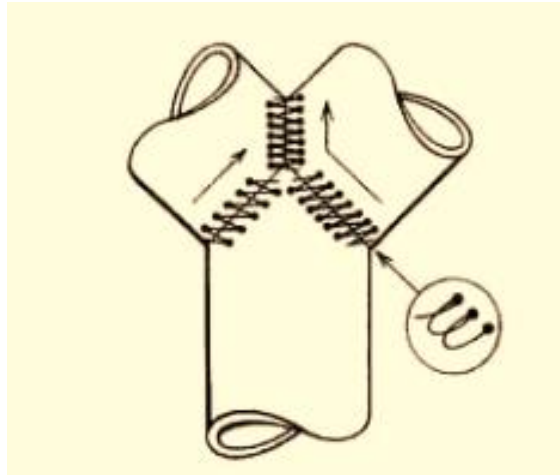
Modèle de tissage pour le soudage d'un joint en Y. [45]
